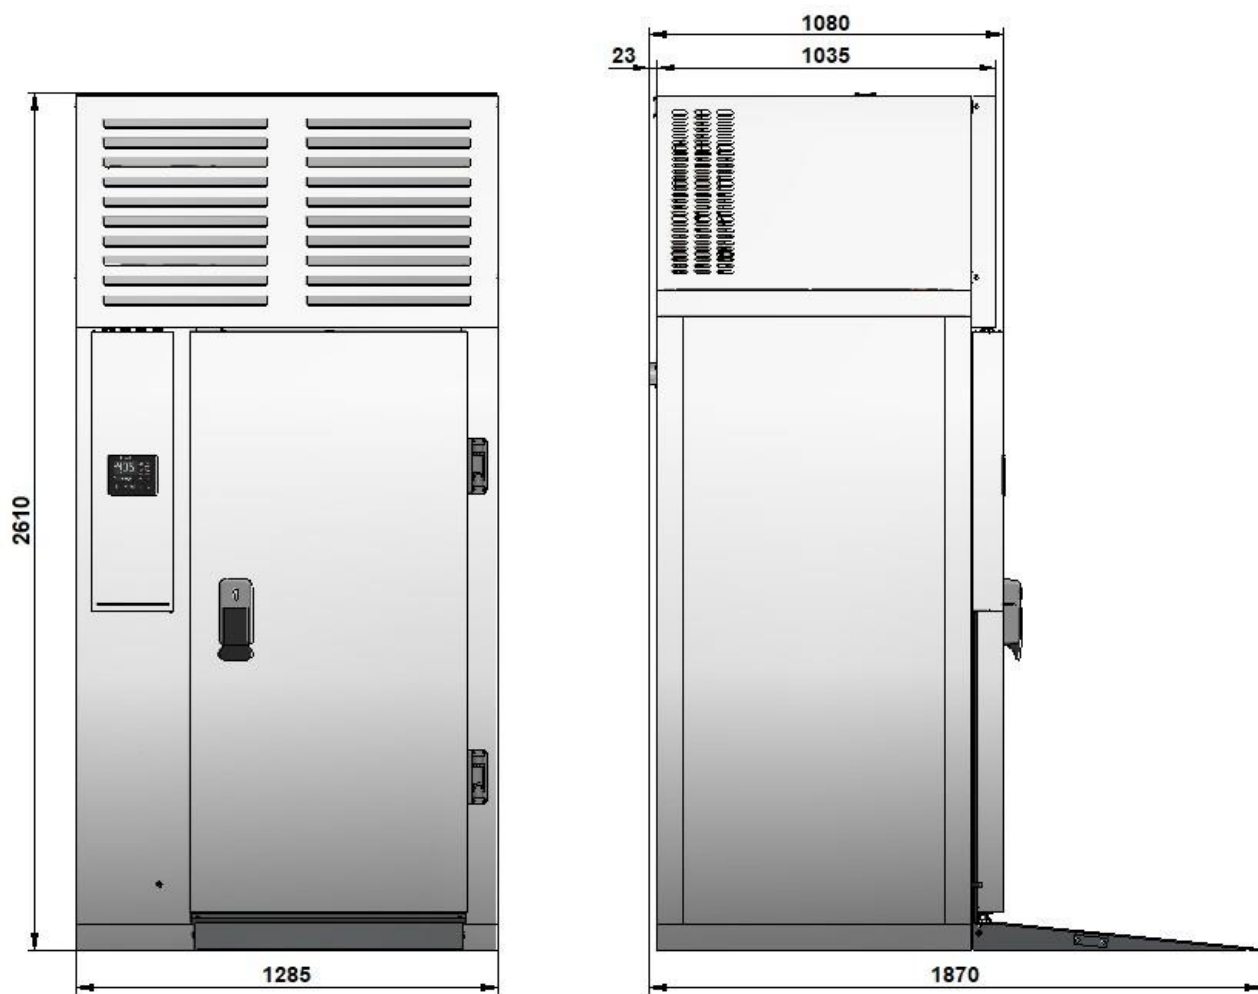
Габаритные размеры камеры ШОКК-20Т-К
